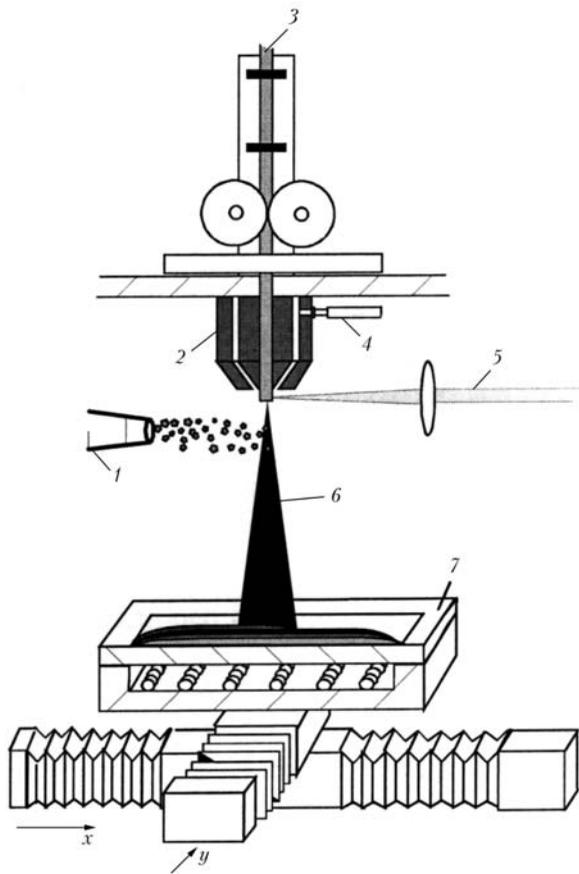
Схема процесса лазерного напыления путем распыления проволоки с дополнительным введением порошковых материалов для получения композитных покрытий: 1 — подача порошка; 2 — сопло; 3 — распыляемая проволока; 4 — газ; 5 — лазерное излучение; 6 — напыляющая струя; 7 — подложка
